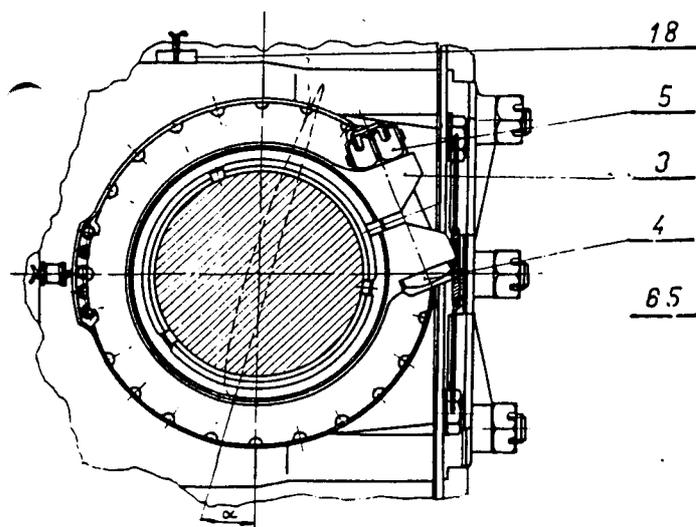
Luftschraube Type V 503 A — Schnitt
